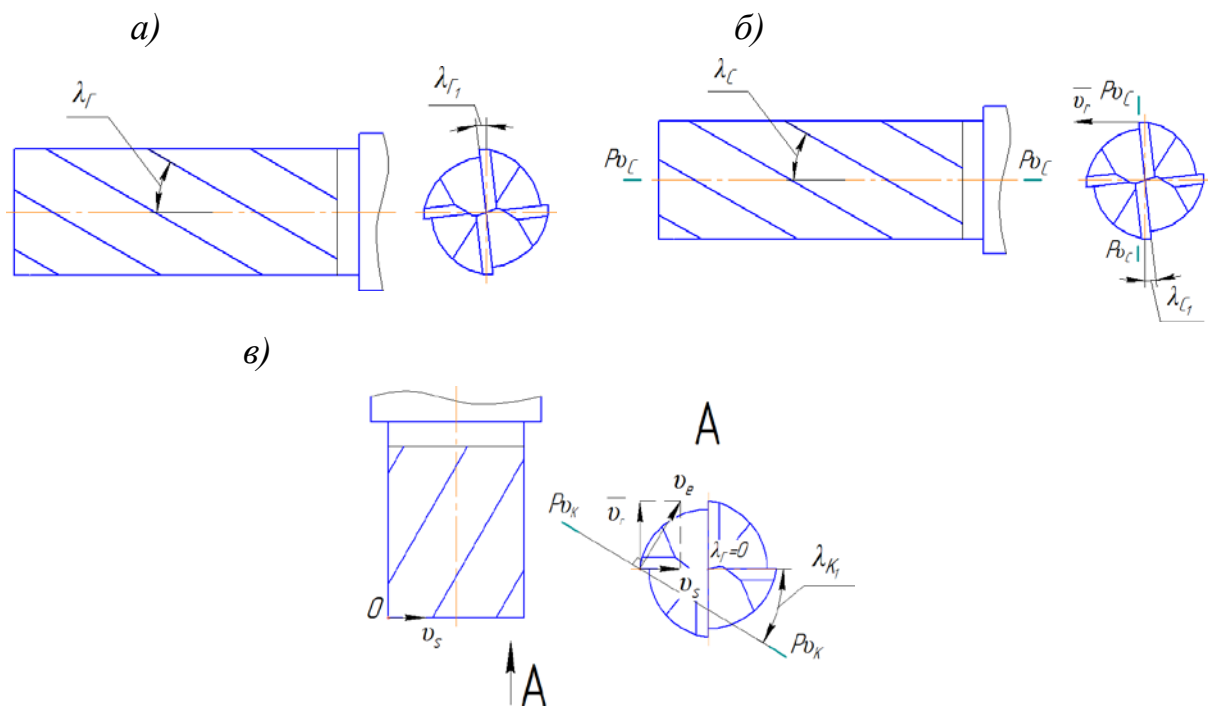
Схема для определения угла наклона режущей кромки инструмента в инструментальной (а), статической (б) и кинематической (в) системах координат
